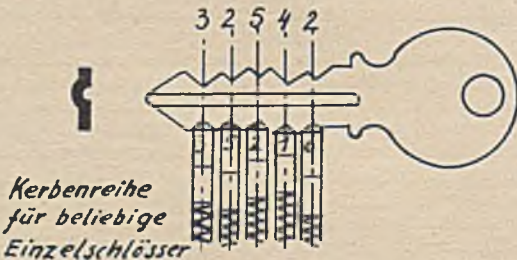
Einzel-schließzylinder für Flachs-schlüssel
